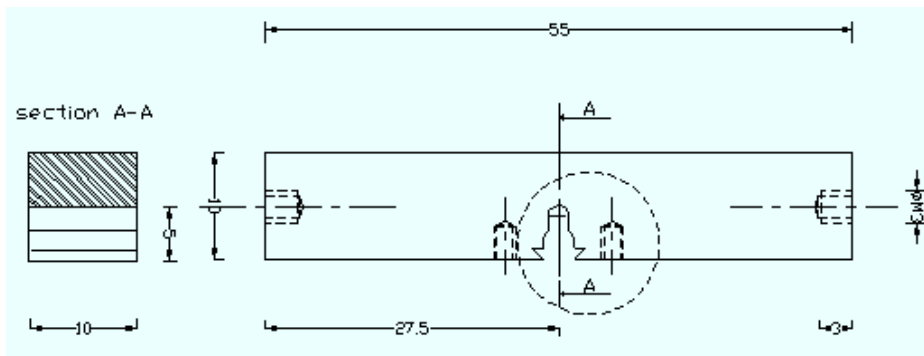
11 : Plan des éprouvettes KCU de section  $10 \times 10 \text{ mm}^2$ .
